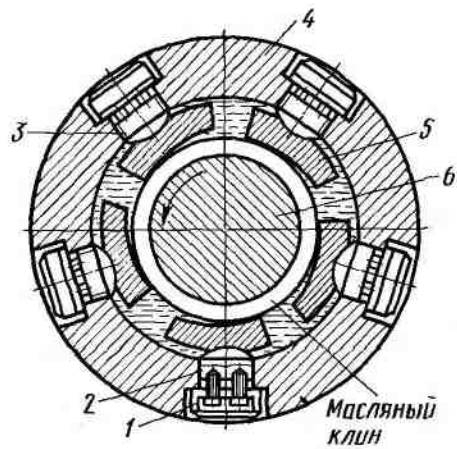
Конструкция гидродинамического подшипника скольжения
